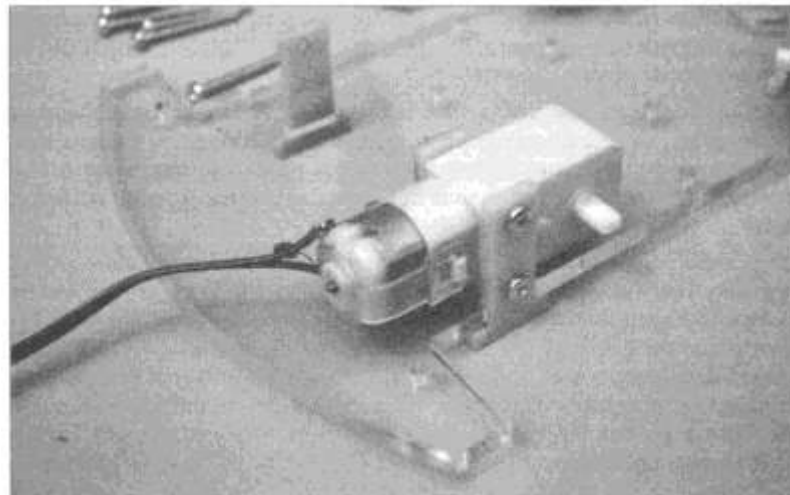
Установка двигателя на T-образные крепления в корпус робота
